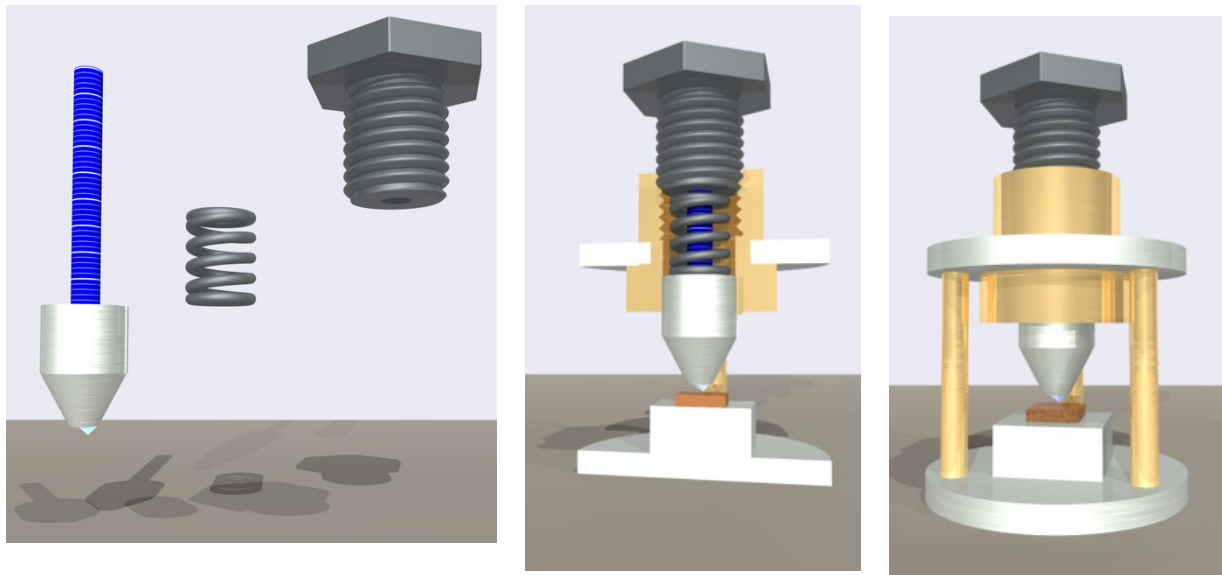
Aufbau der Härteprüfmaschine: Stößel mit Skala, Feder und Schraube (links), Schnitt durch den Aufbau (Mitte) und 3D-Ansicht (rechts).
